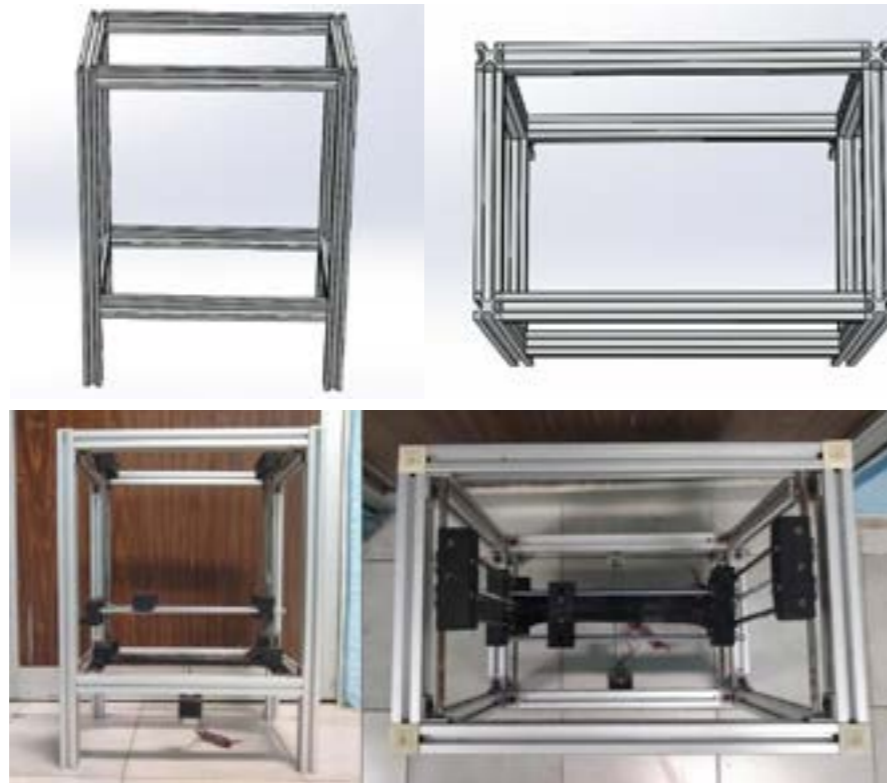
Construcción de la estructura con perfiles de Aluminio.
